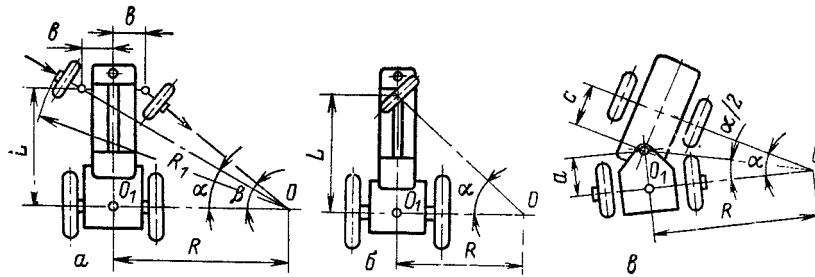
Кинематика поворота колесных тракторов и автомобилей:
